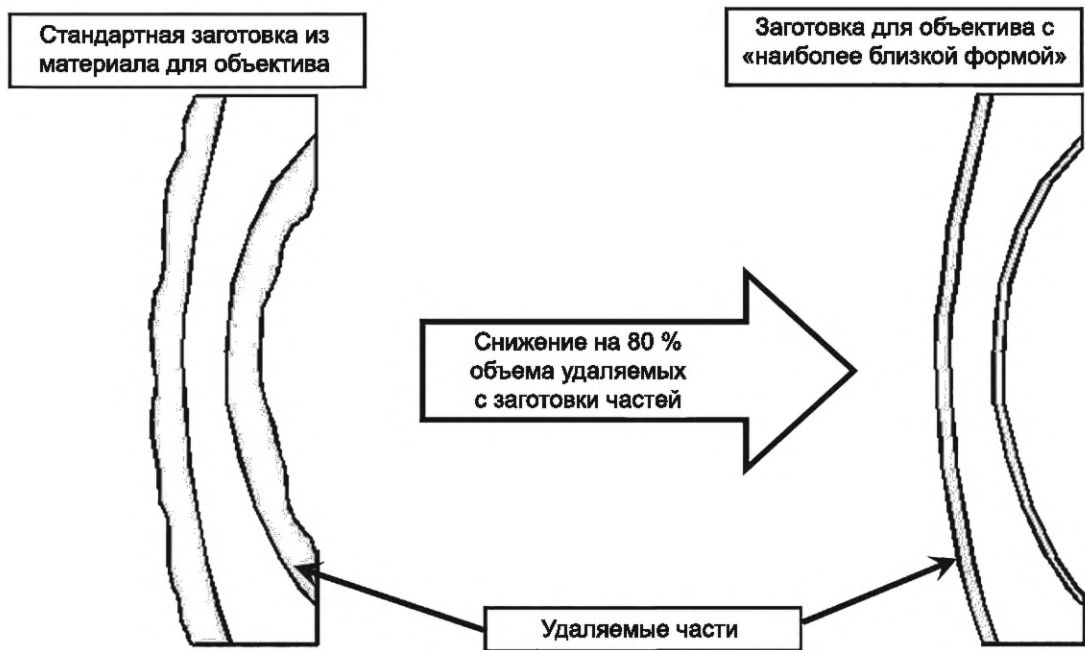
Заготовка с «наиболее близкой формой» для объектива
